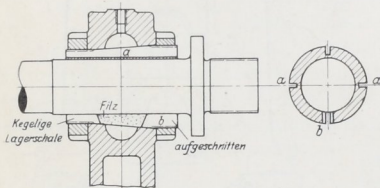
Nachstellbares Lager an Werkzeugmaschinen.
